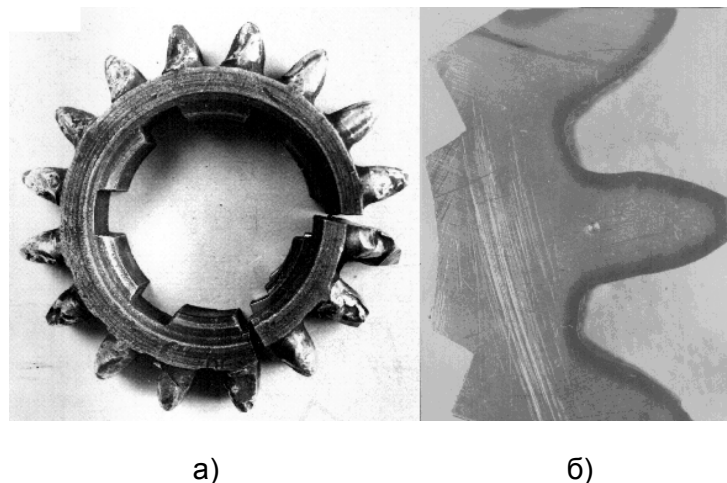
Выкрашивание зубьев шестерни коробки передач вертикально-фрезерного станка (а) из-за неполного зацепления. разрушение началось от цементированного слоя, глубиной 1 мм (б).
